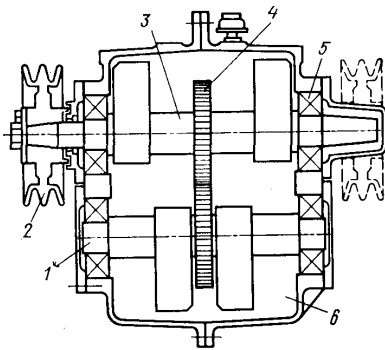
Двухвальный виброблок: 1,3 – ведомый и ведущий вал с дебалансами; 2 – приводной шкив; 4 – зубчатая передача; 5 – подшипники; 6 – масляная ванна.
